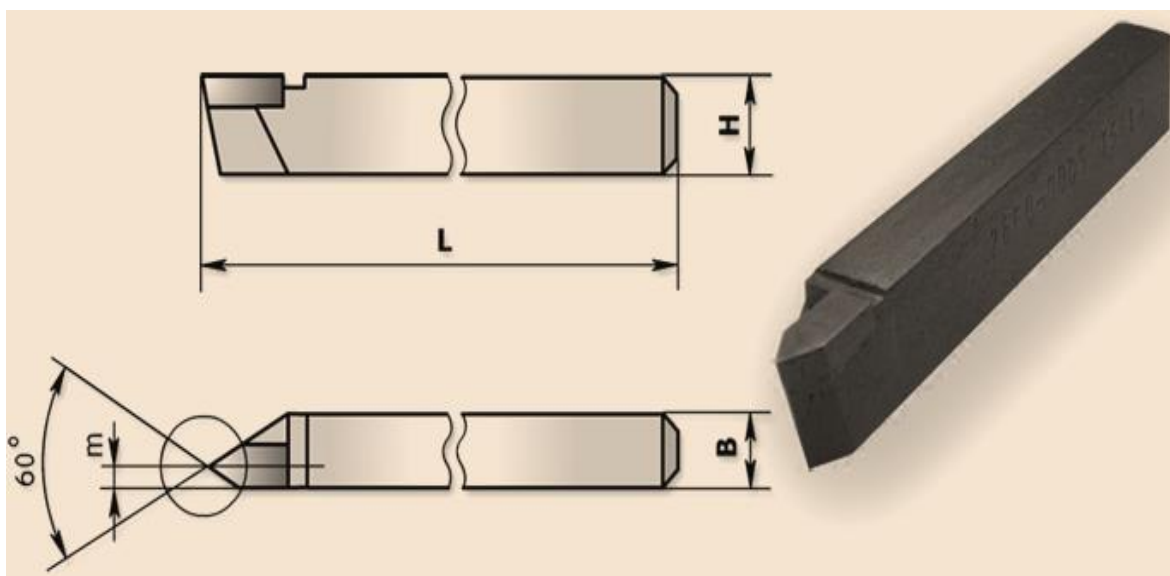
Резцы токарные резьбовые предназначенные для нарезания наружной резьбы
